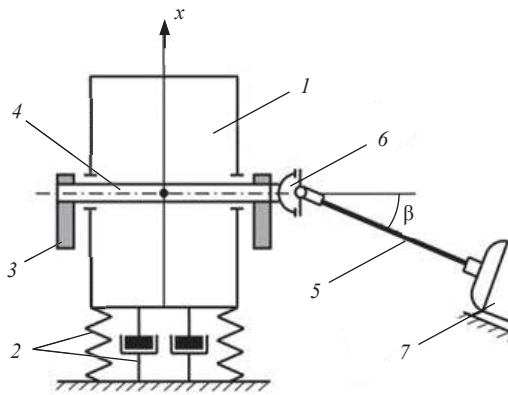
Инерционная вибромашина с карданным валом в трансмиссии привода вращения вибровозбудителя: 1 – рабочий орган; 2 – упругие опоры (подвеска); 3 – дебаланс вибровозбудителя; 4 – вал вибровозбудителя; 5 – приводной вал; 6 – универсальный шарнир (шарнир Гука); 7 – электродвигатель
